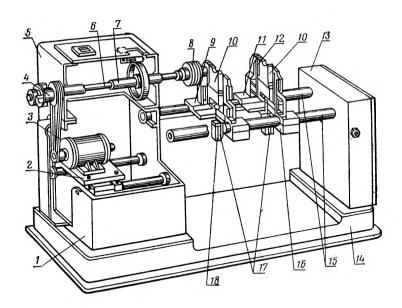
Динамическая балансировочная машина БМ-У4 модели 4274; I и I3— стойки; 2— консольная плита; 3— клиноременная передача; 4 и 8— пружинные муфты; 5— шпиндельная бабка; 6— приводной вал; 7— шпиндель; 9 и 11— опоры люлек; 10— люлька; 12— стальная лента; 14— плита; 15— трубчатые направляющие; 16— демпфер; 17— электромагниты; 18— кронштейи.
